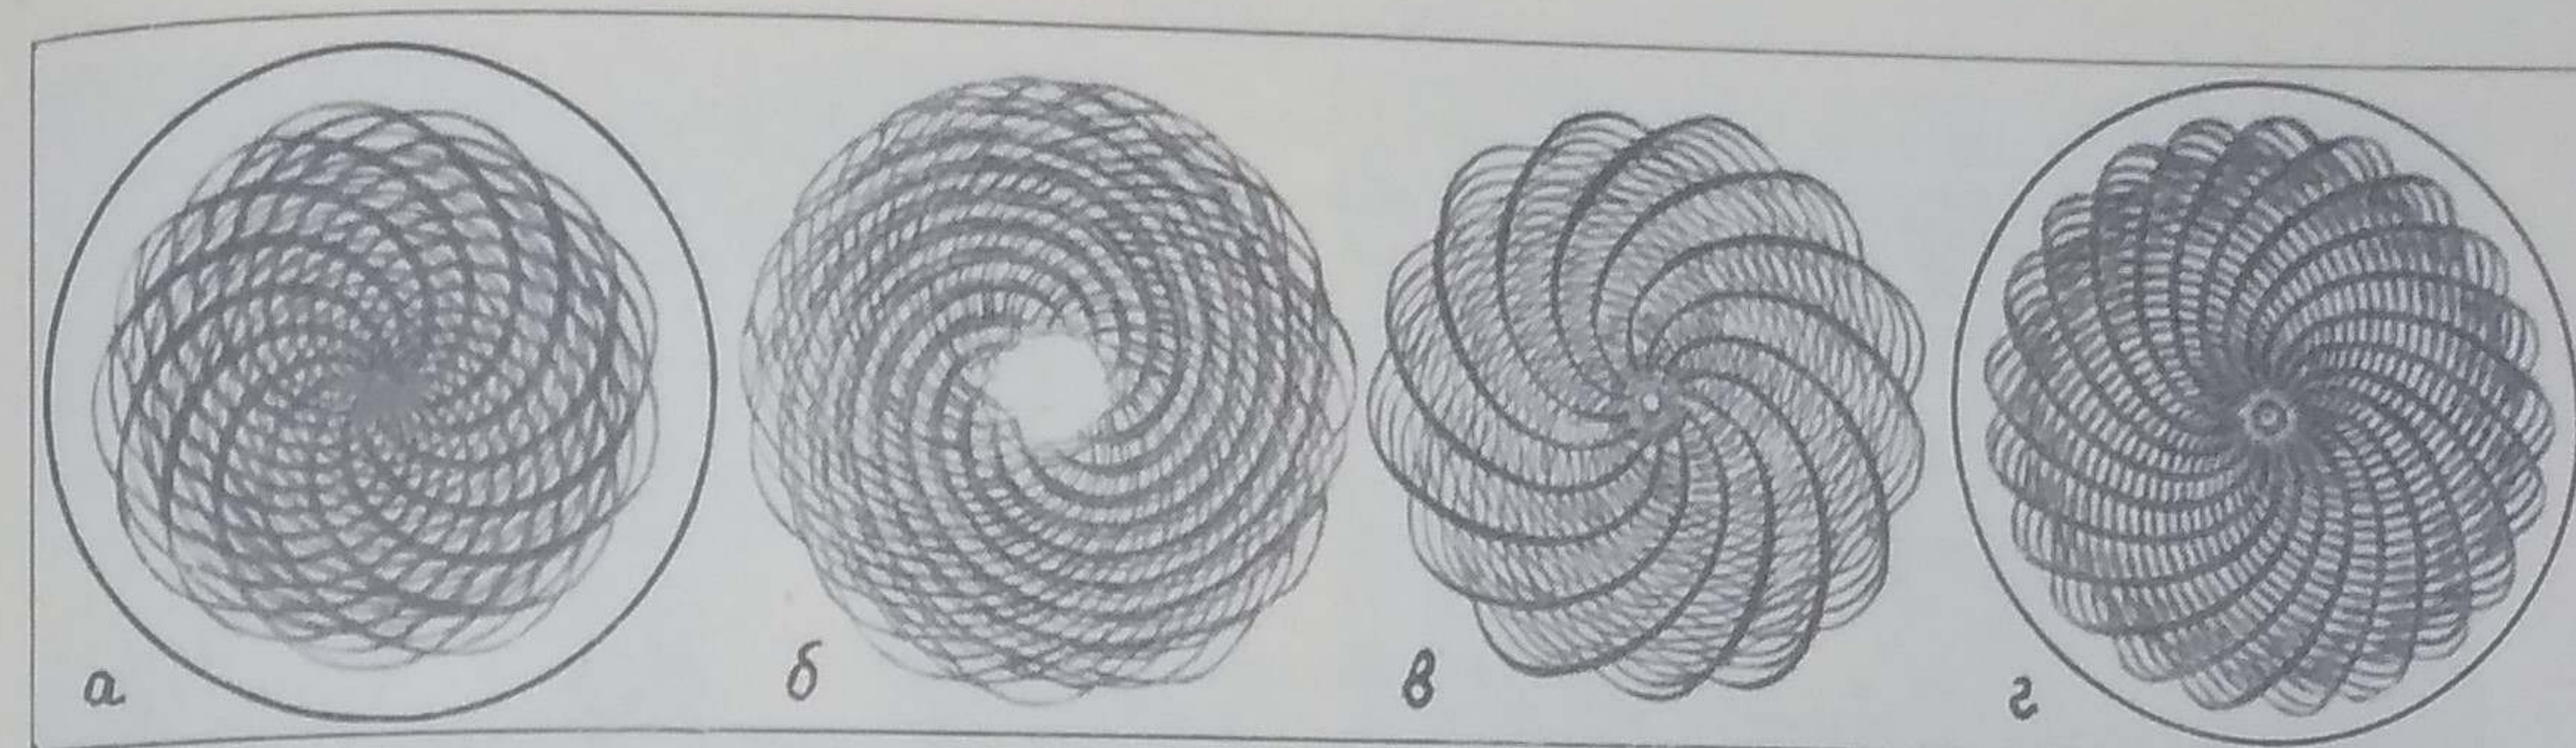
Рисунки, получающиеся при виброобкатывании торцевых поверхностей при числе оборотов заготовки (об/мин):
